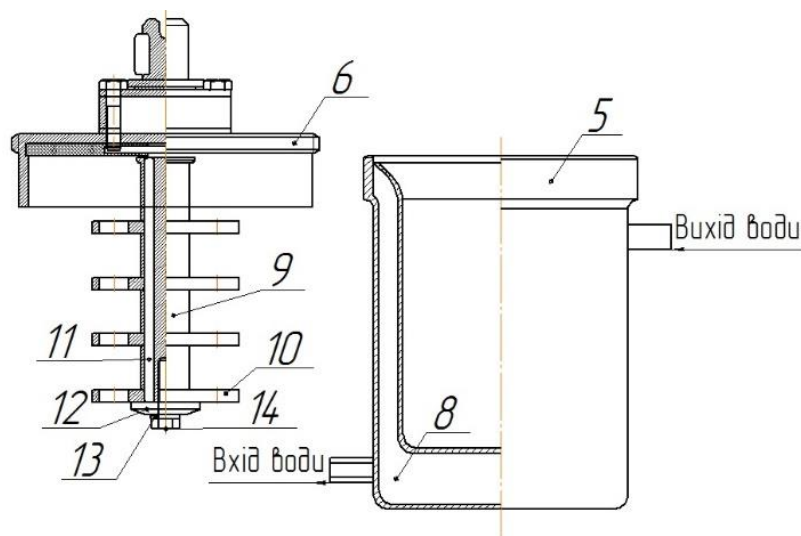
Робоча камера: 5 – стакан; 6 – кришка стакану; 8 – сорочка охолодження; 9 – вал; 10 – диски; 11 – шпонка; 12 – шайба; 13 – шайба Гровера; 14 – болт.
